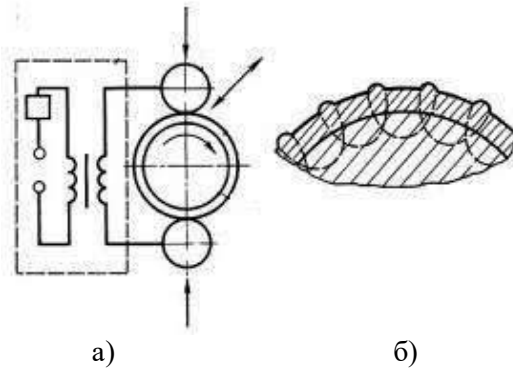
Схема наварювання стрічки на деталь типу вал (а) і перекриття імпульсів під час наварювання (б)
